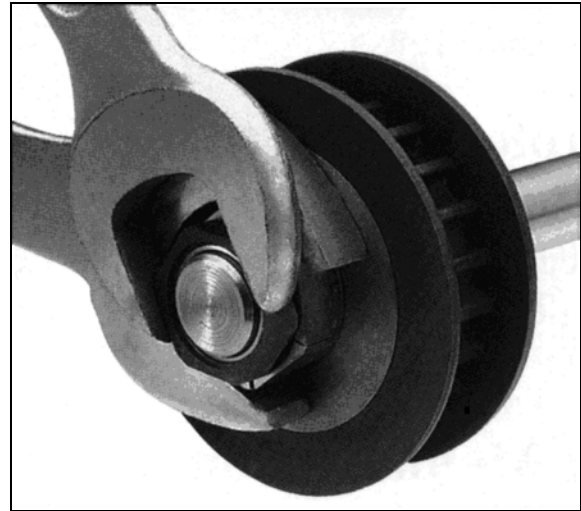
SERRAGE DE LA BAGUE SANS CLAVETTE
